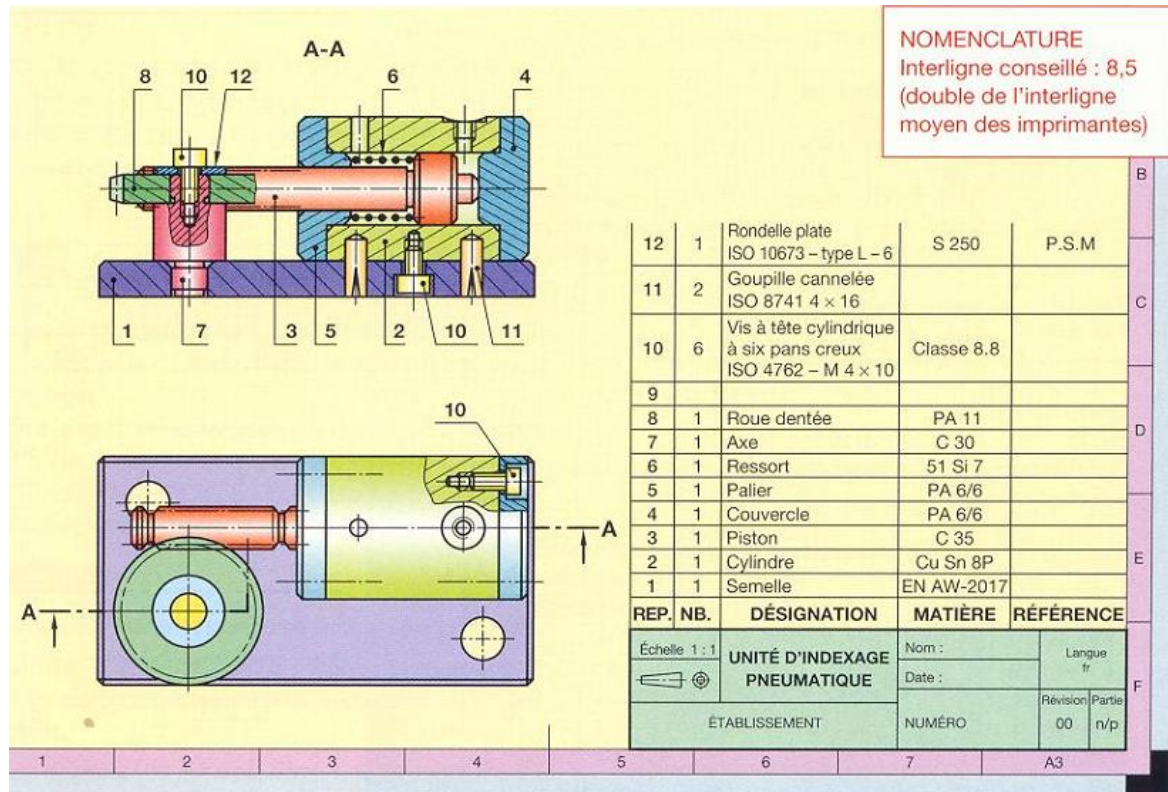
Dessin d'ensemble, Cartouche, Nomenclature.
